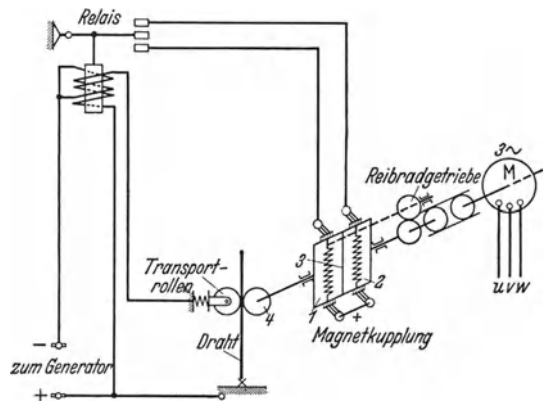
Weitere Steuerungen von selbsttätigen Lichtbogenschweißeinrichtungen.
